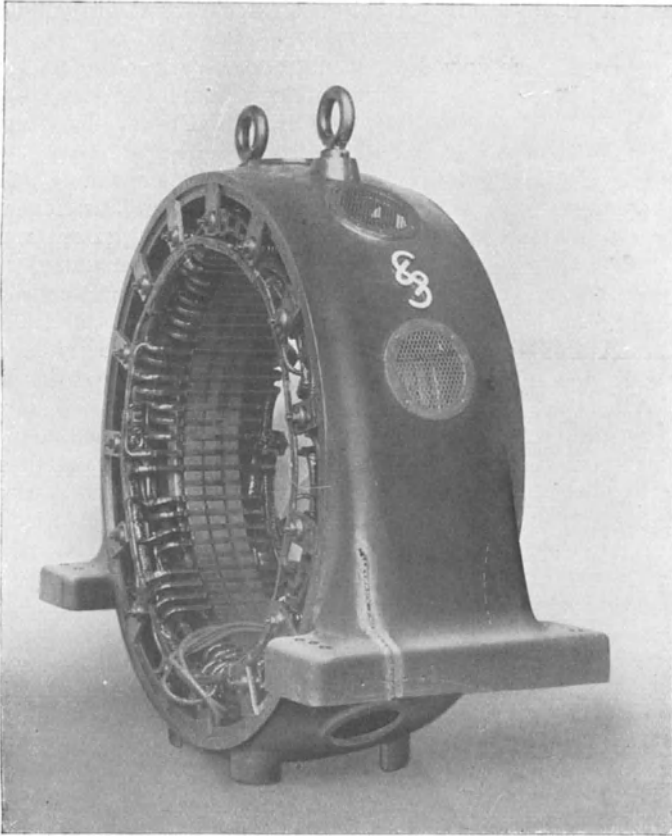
Schweißung am Fuß eines Generatorgehäuses.
